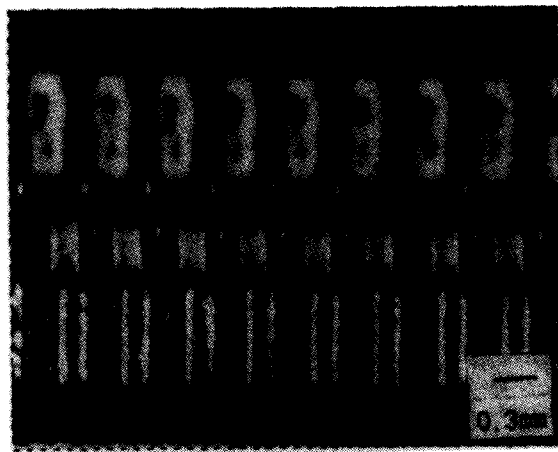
레이저 솔더링 접합 형상(Sn-37Pb solder paste, 5.9W, 400 ms)
